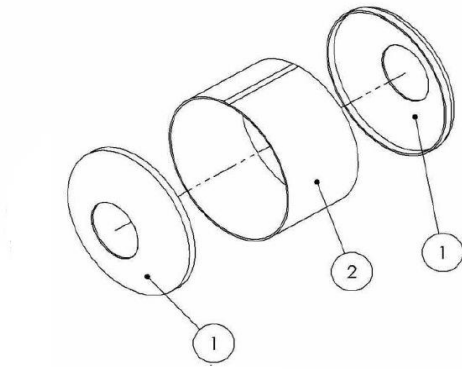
Vista explotada del componente. 1) casquetes embutidos con bocas de inspección; 2) virola cilíndrica con soldadura longitudinal.
